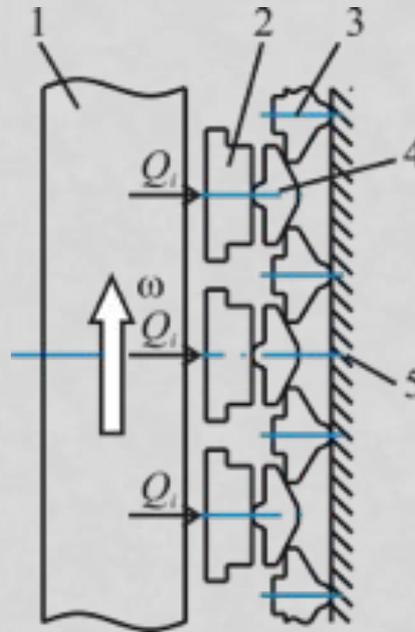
Конструктивная схема упорного подшипника скольжения с упругим выравнивающим устройством:
